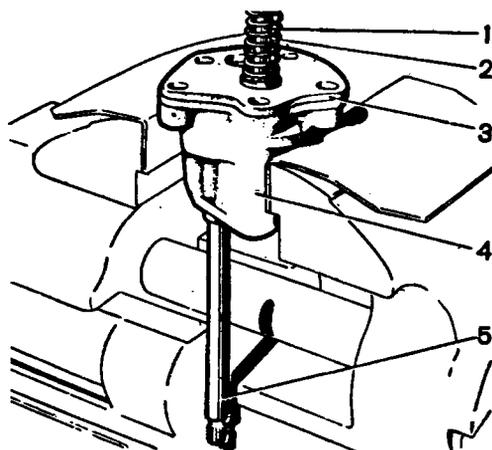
Разборка масляного насоса: 1 - редукционный клапан; 2 - пружина; 3 - крышка; 4 - корпус; 5 - валик
